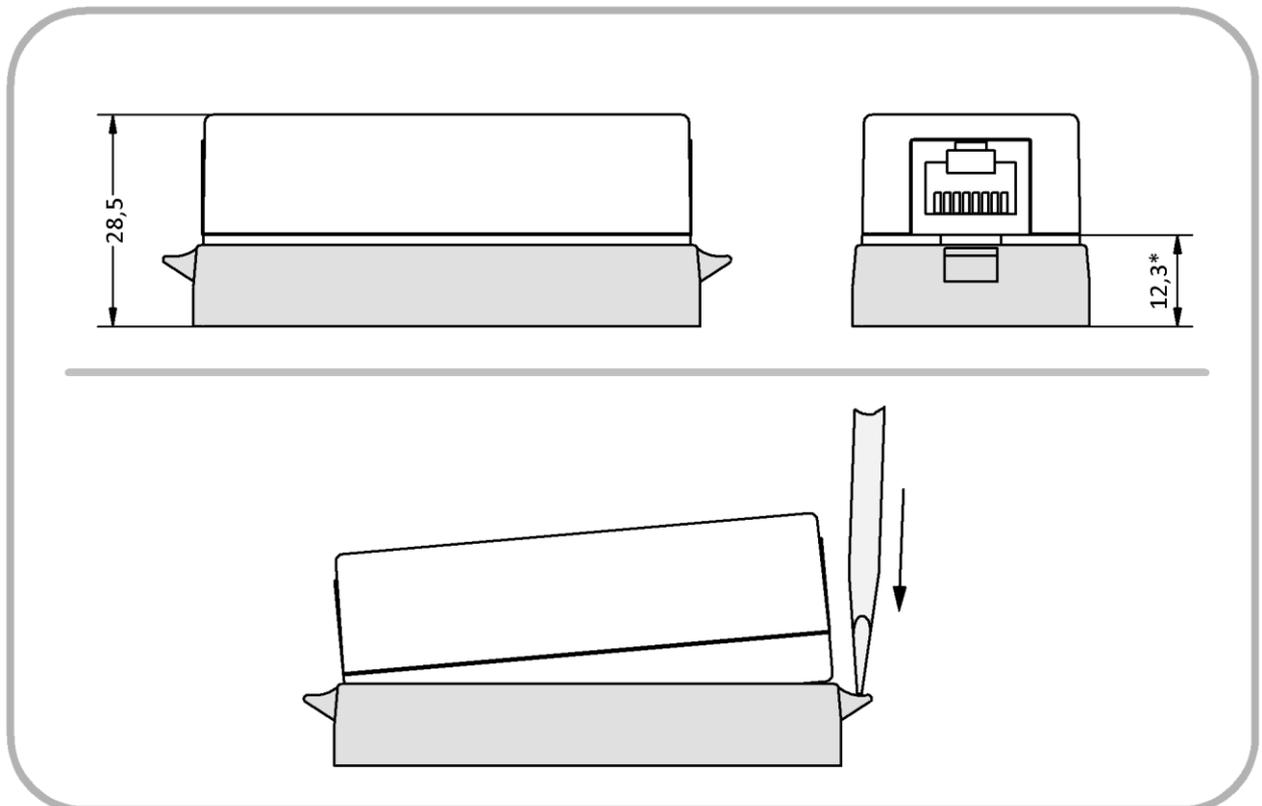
Z-6W - Montage Maße und Entriegelung. Alle Maßangaben in Millimetern.
